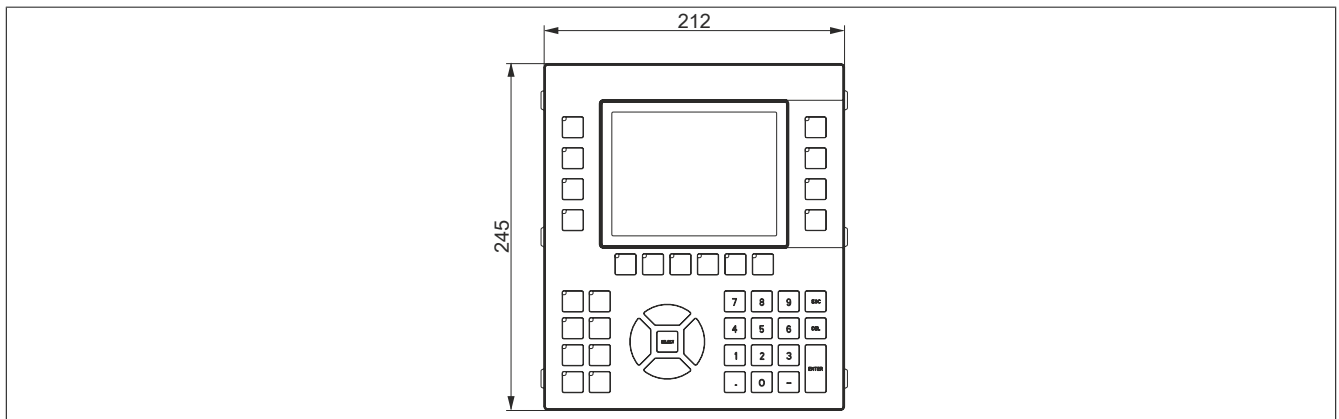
5AP1151.0573-000 - Abmessungen
